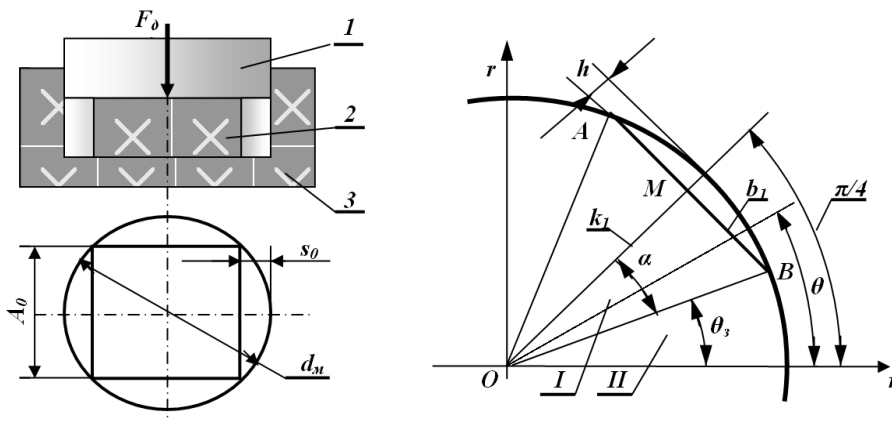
Схема осадки квадратной заготовки в цилиндрической матрице (а): 1 – пуансон, 2 – заготовка, 3 – матрица; разбивка заготовки на области (б)
